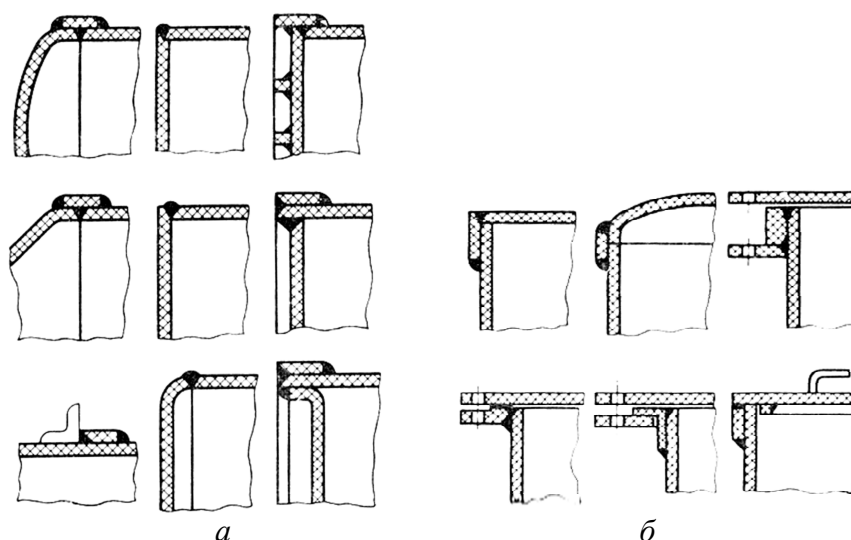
Примеры конструирования соединений дна (*а*) и крышки (*б*) с корпусом сосуда
